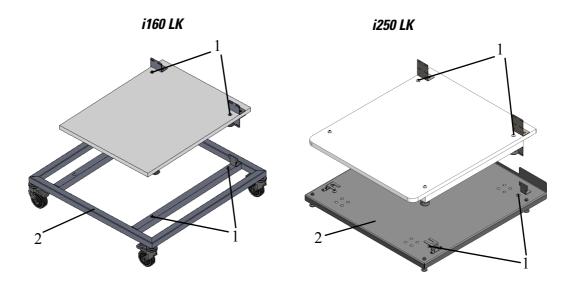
Telaio di sovrapposizione e supporto con elementi di sovrapposizione
